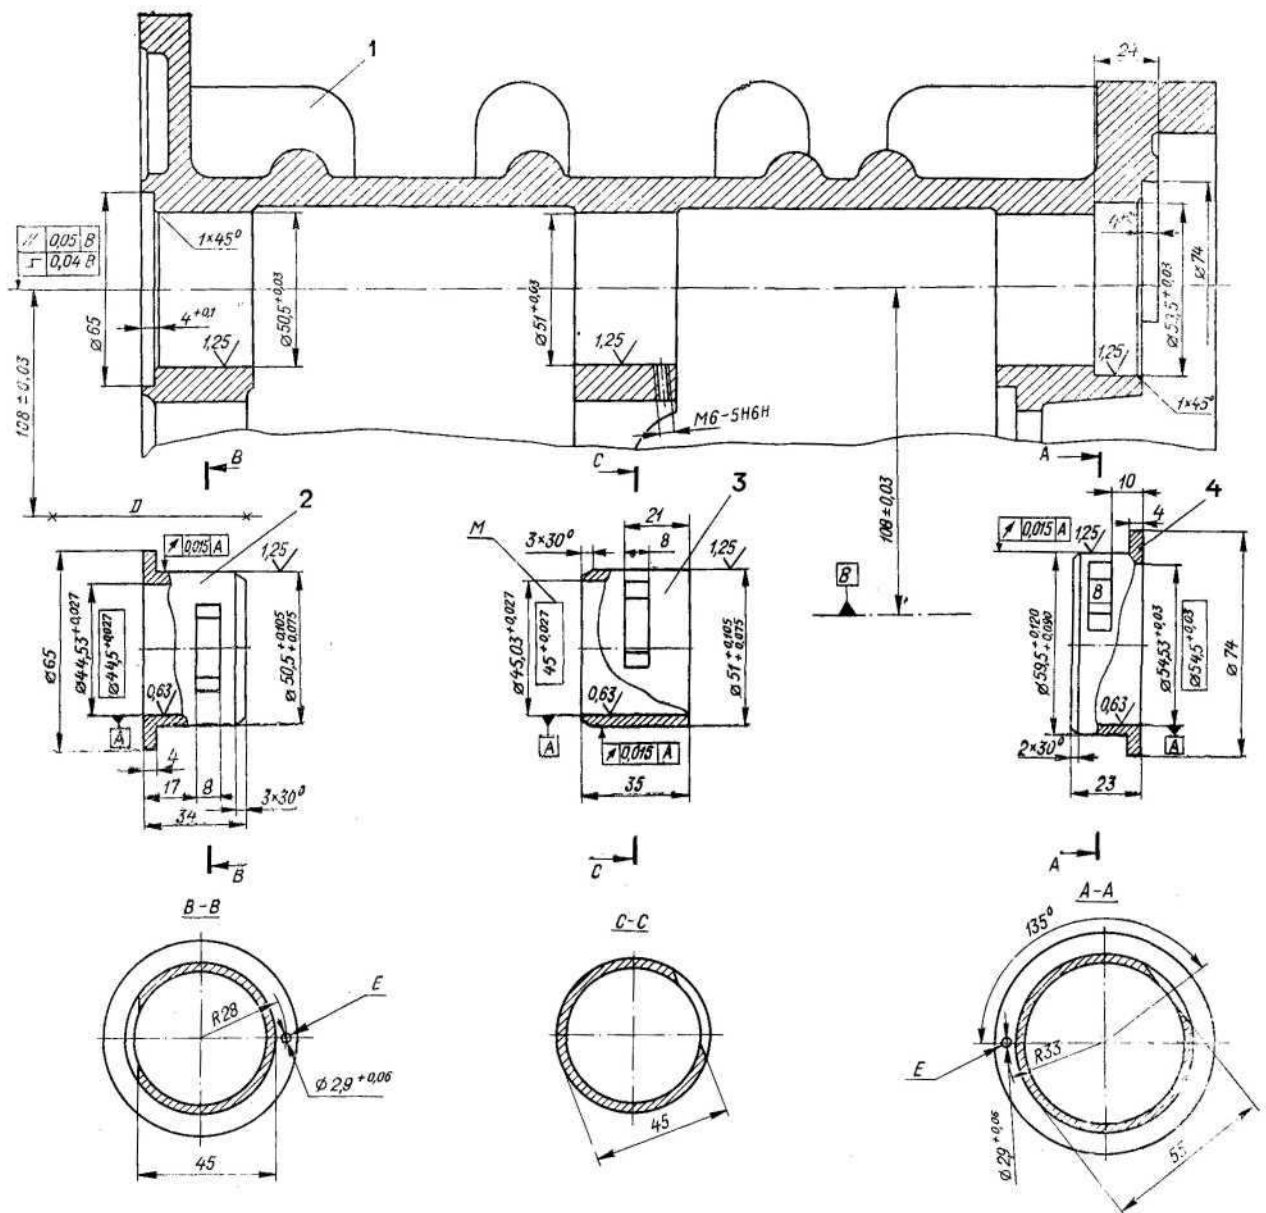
Расточка картера двигателя под ремонтные подшипники распределительного вала:
